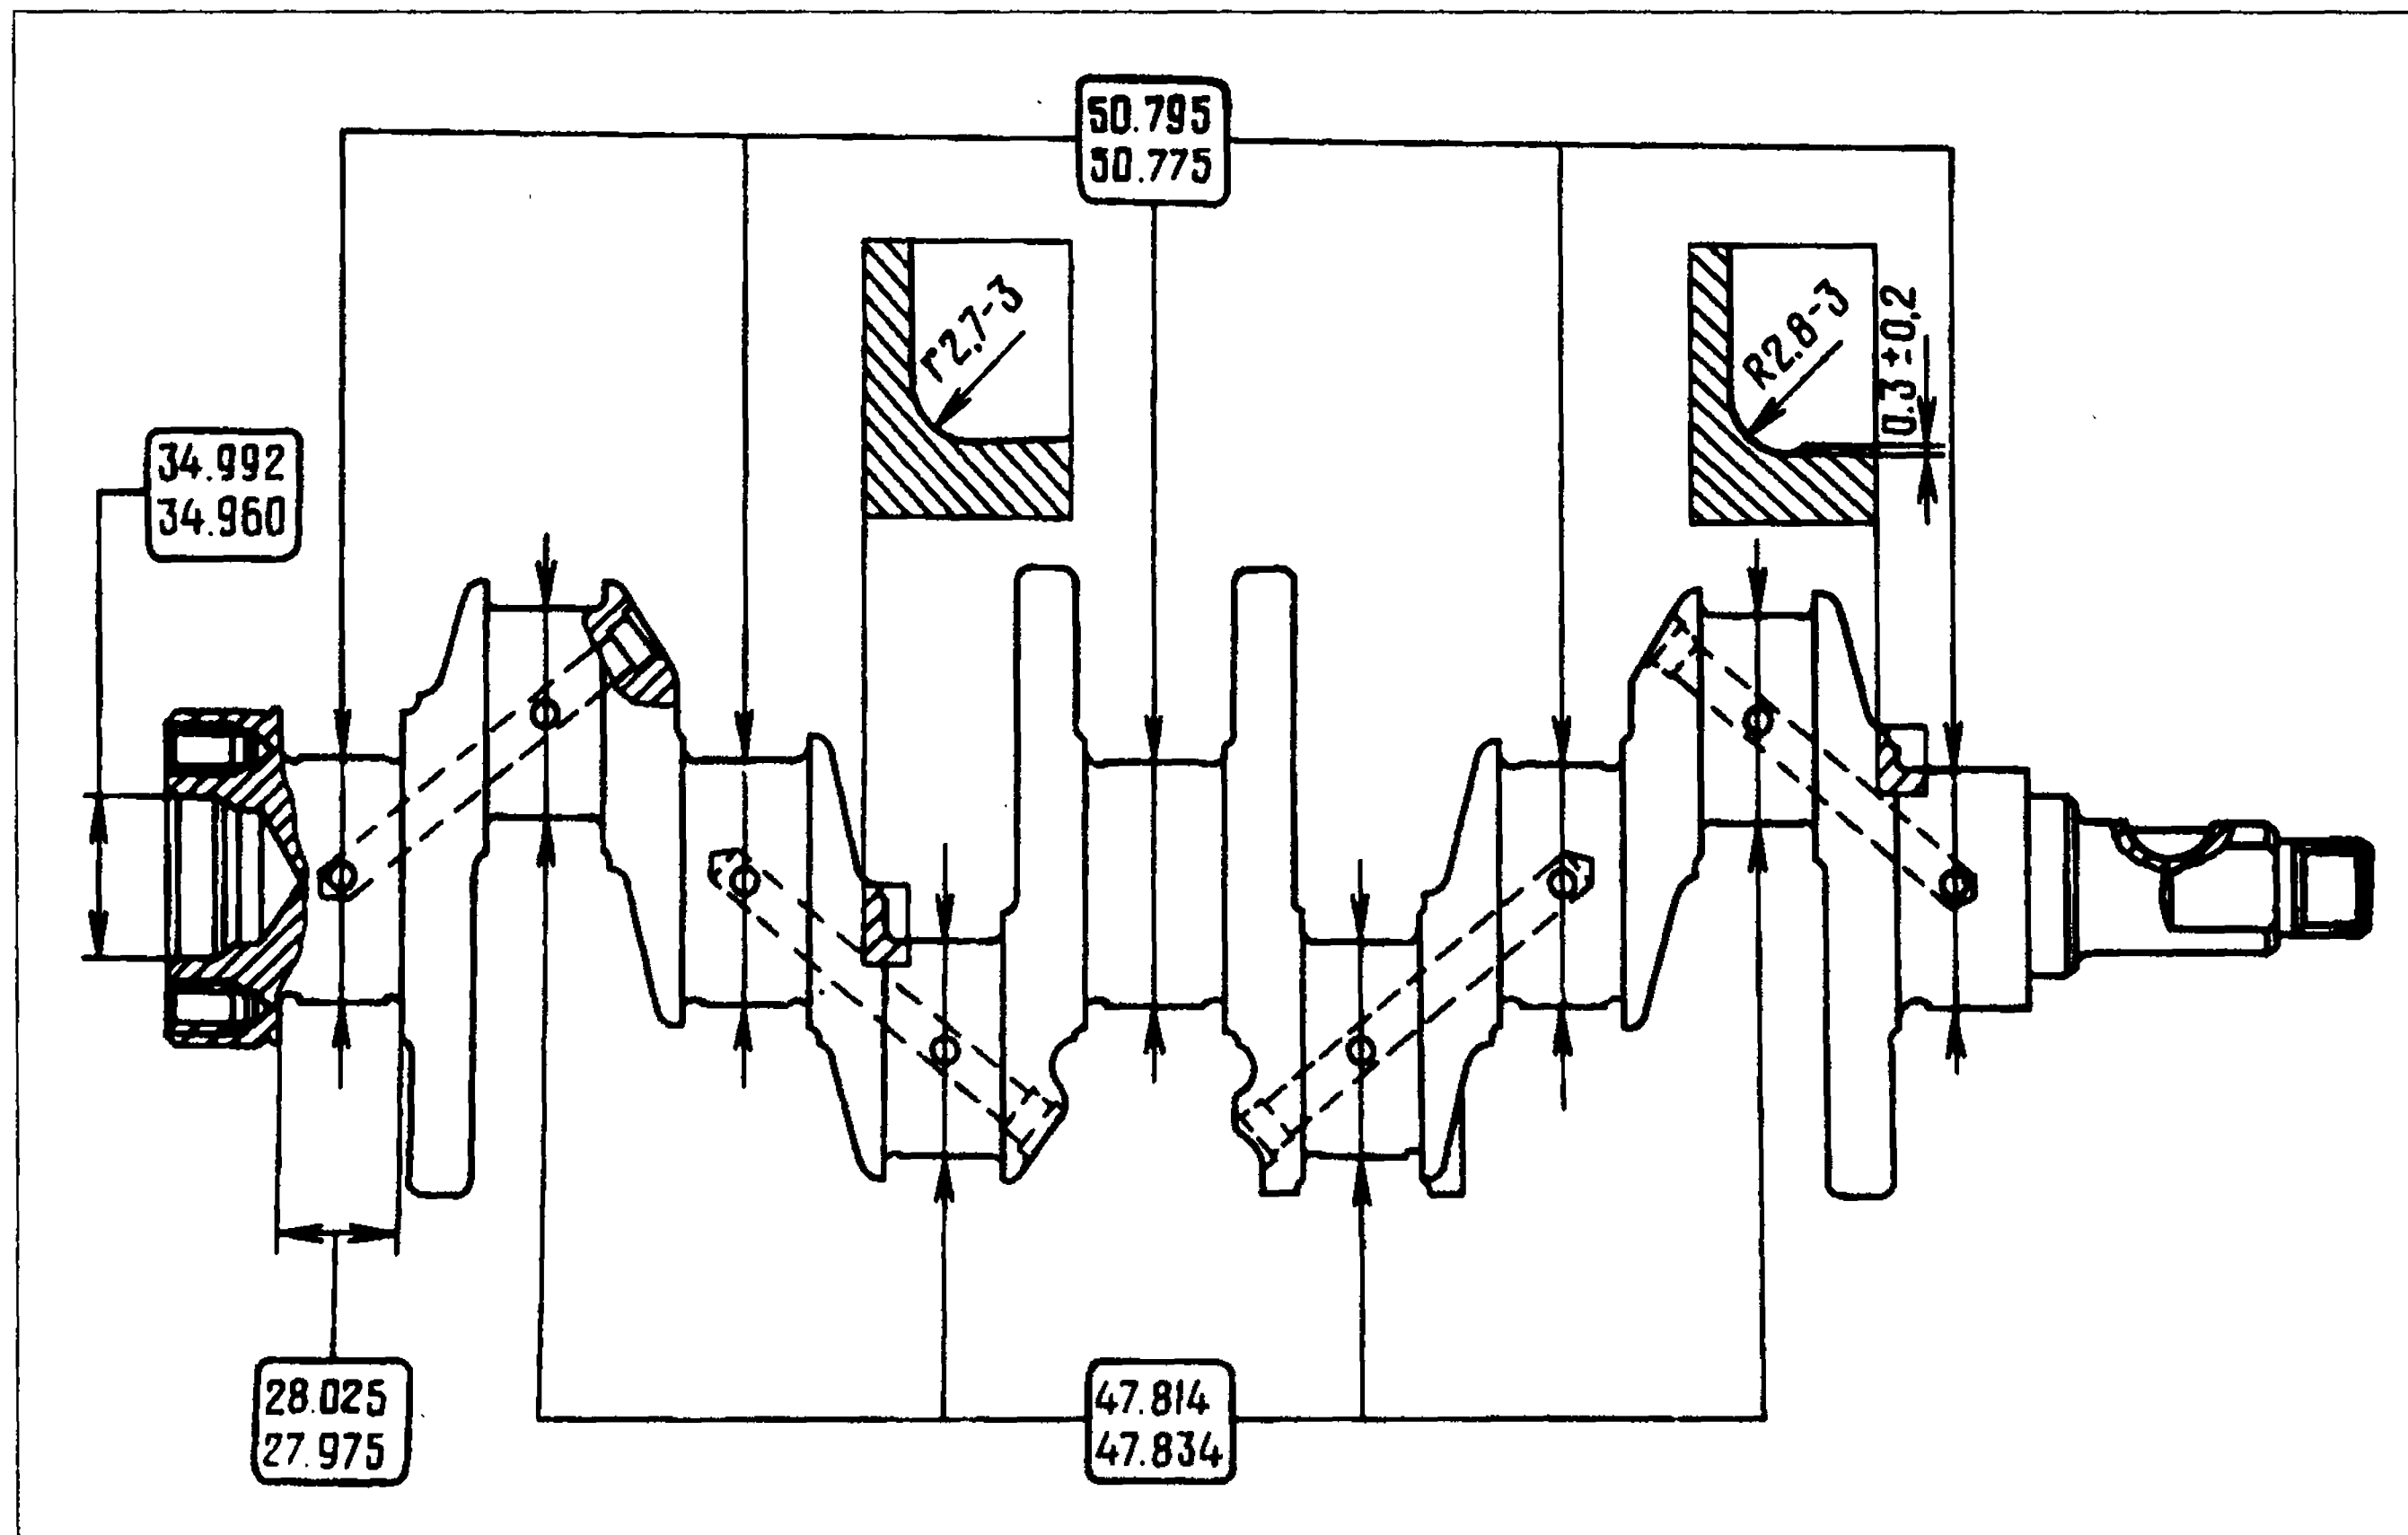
Основные размеры шатунных и коренных шеек коленчатого вала и их галтелей
